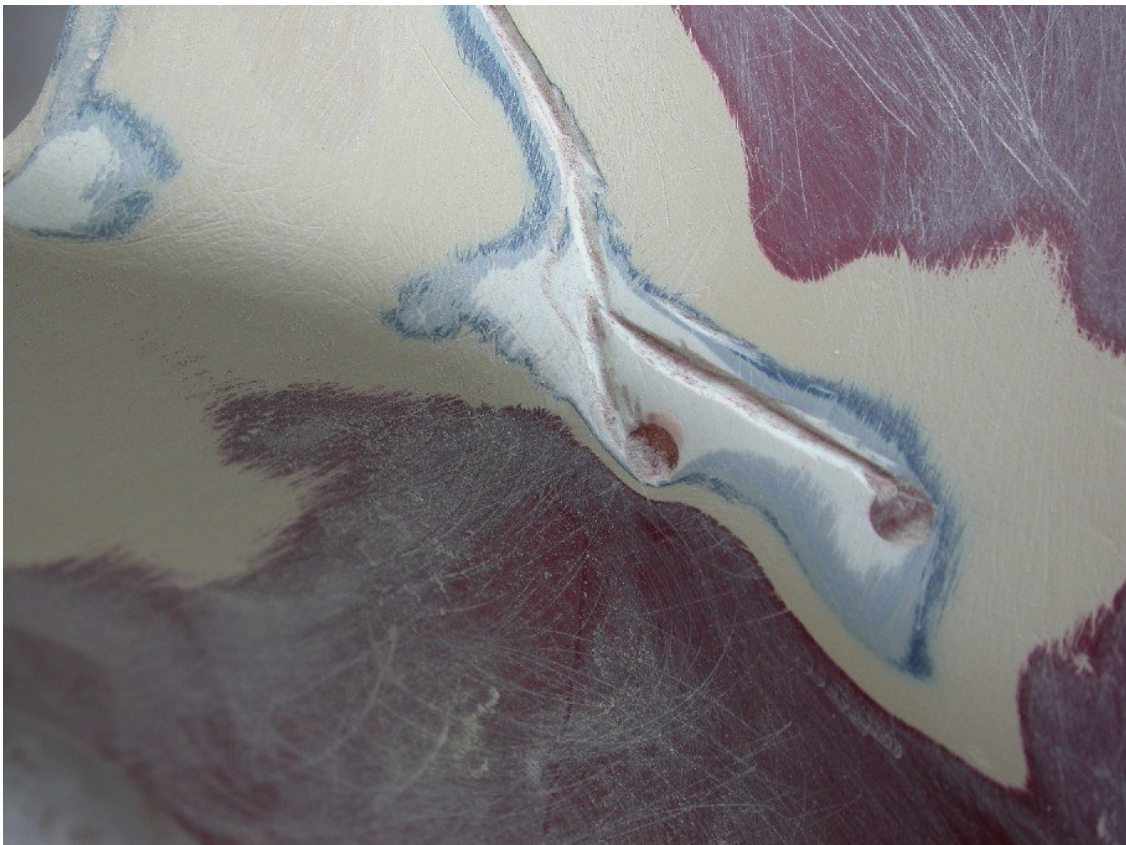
auf der Außenseite v-förmig ausgeschliffener Riss und angebohrte Rissenden vor dem Verspachteln (aber nach dem Laminieren; Bohrungen sind voll Epoxydharz gelaufen)
